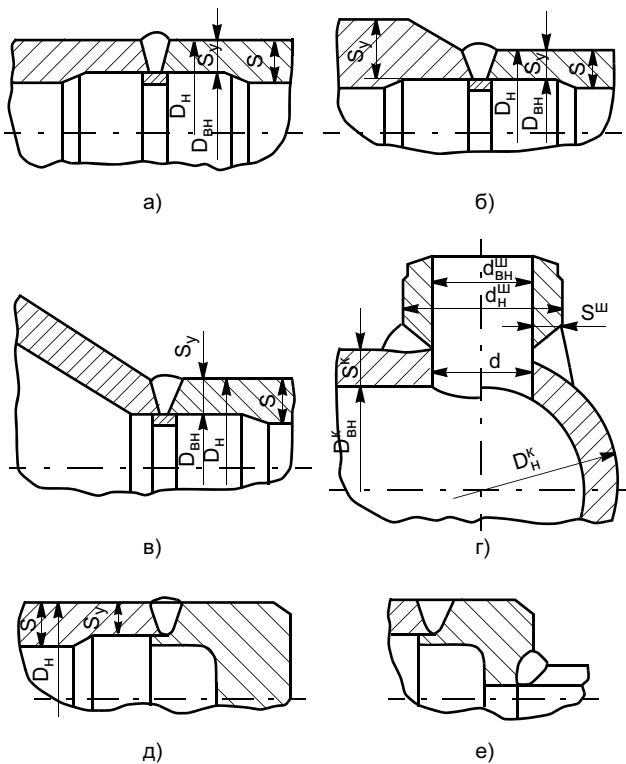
Типы сварных соединений паропроводов: а — стыковое сварное соединение трубных элементов с одинаковой толщиной стенки — СССР; б — стыковое сварное соединение разнотолщинных трубных элементов — СССР_{ртз}; в — стыковое сварное соединение трубы с коническим переходом — СССР_{кл}; г — тройниковое (штуцерное) сварное соединение — ТСС (ШСС); д — стыковое сварное соединение трубы с донышком — СССР_д; е — штуцерное сварное соединение патрубка с донышком — ШСС_д
